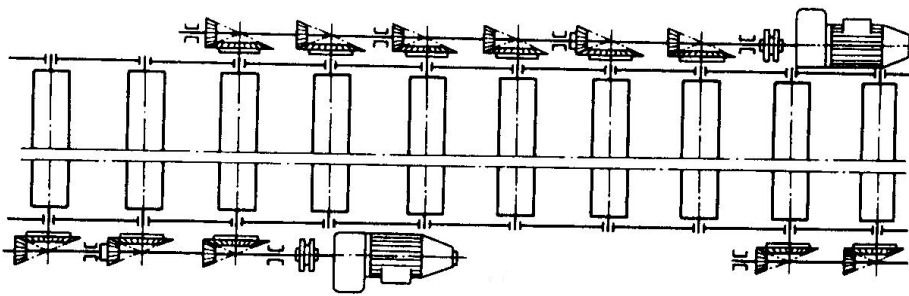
Схема привода роликового конвейера с продольным валом и коническими зубчатыми передачами
